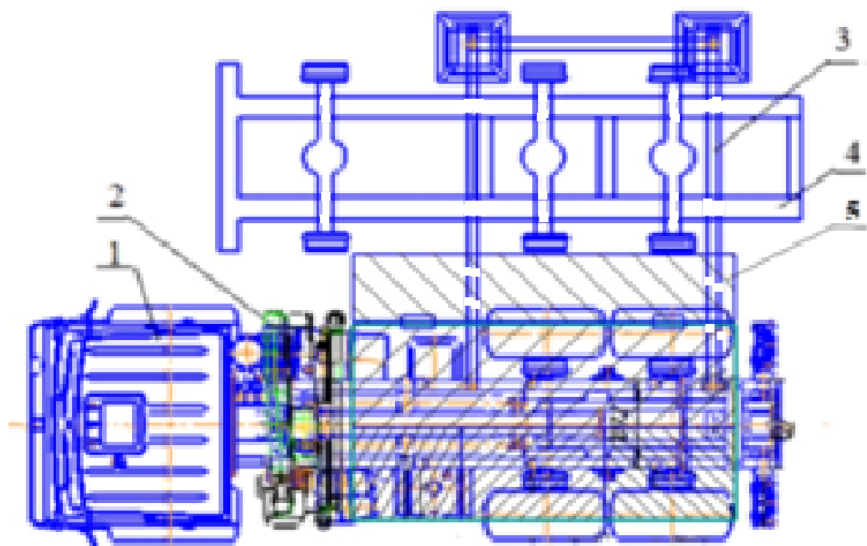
Грузовой автомобиль МАЗ-631705 с КМУ и сборной конструкцией:
